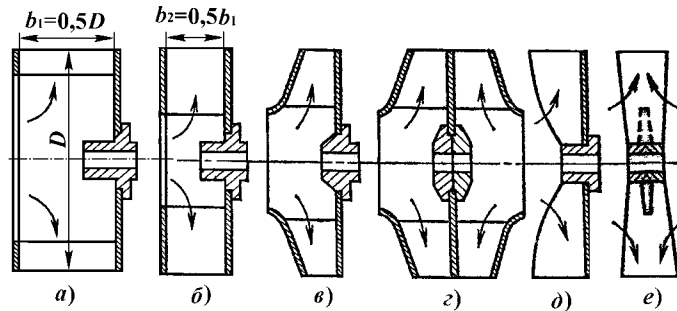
Конструкции рабочих колёс вентиляторов:
